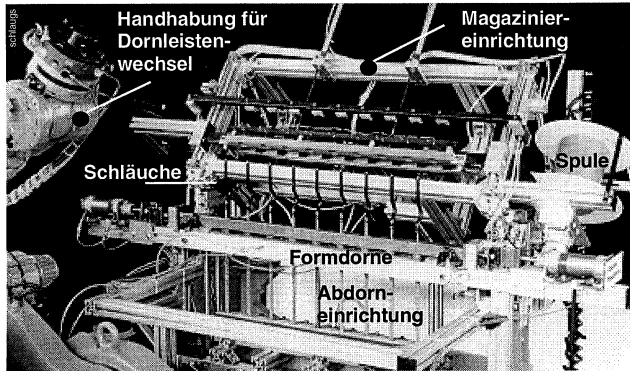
Pilotanlage zur Bereitstellung formlabiler Formschläuche
